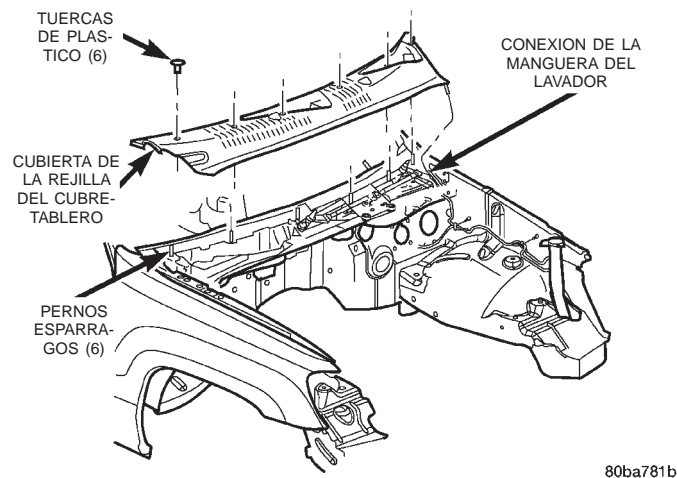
Desmontaje e instalación de la cubierta de la rejilla del cubretablero
